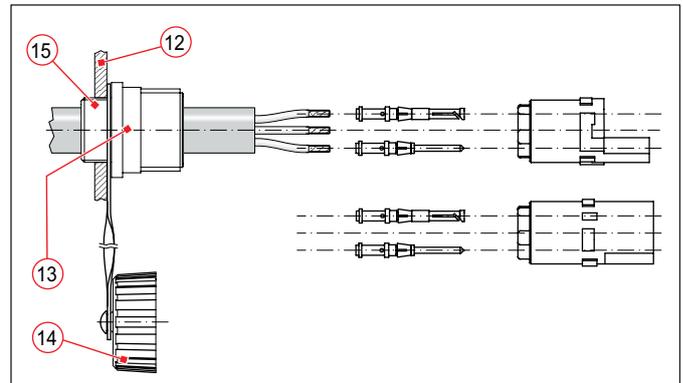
Montagebeispiel für Dosen mit Gewinde an eine Montagewand (gilt analog auch für Stecker mit Gewinde)
